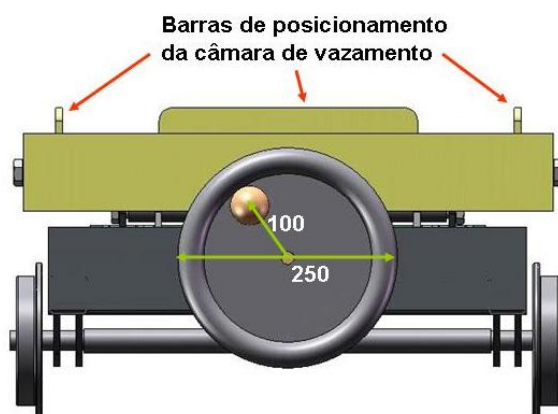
Vista de frente do carro de elevação da câmara de vazamento inferior.
